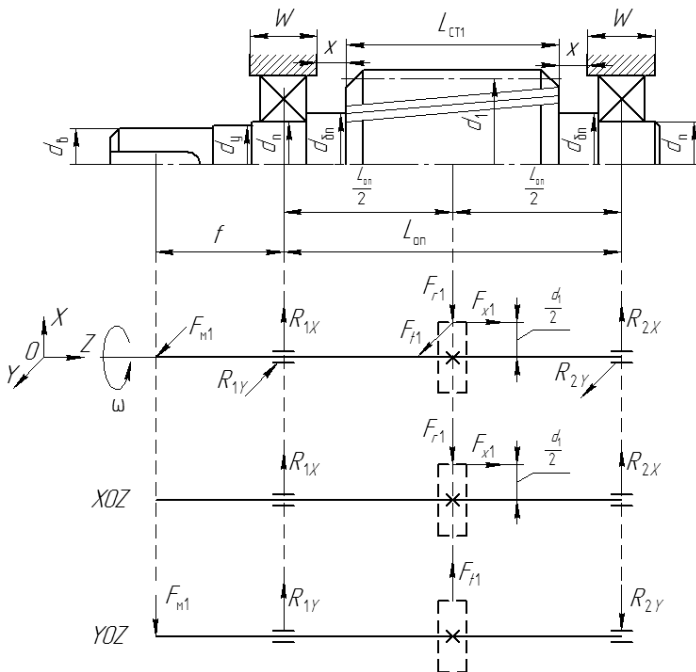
Схема нагружения быстроходного вала цилиндрического косозубого одноступенчатого редуктора
